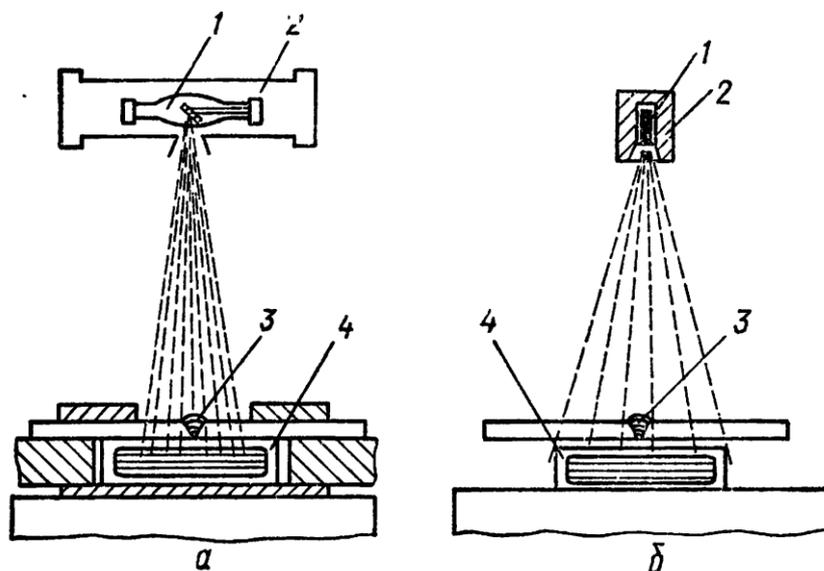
Схемы просвечивания сварочного шва рентгеновскими (а) и гамма-лучами(б): 1 — лампы; 2 — контейнеры; 3 — сварной шов; 4 — пленка
